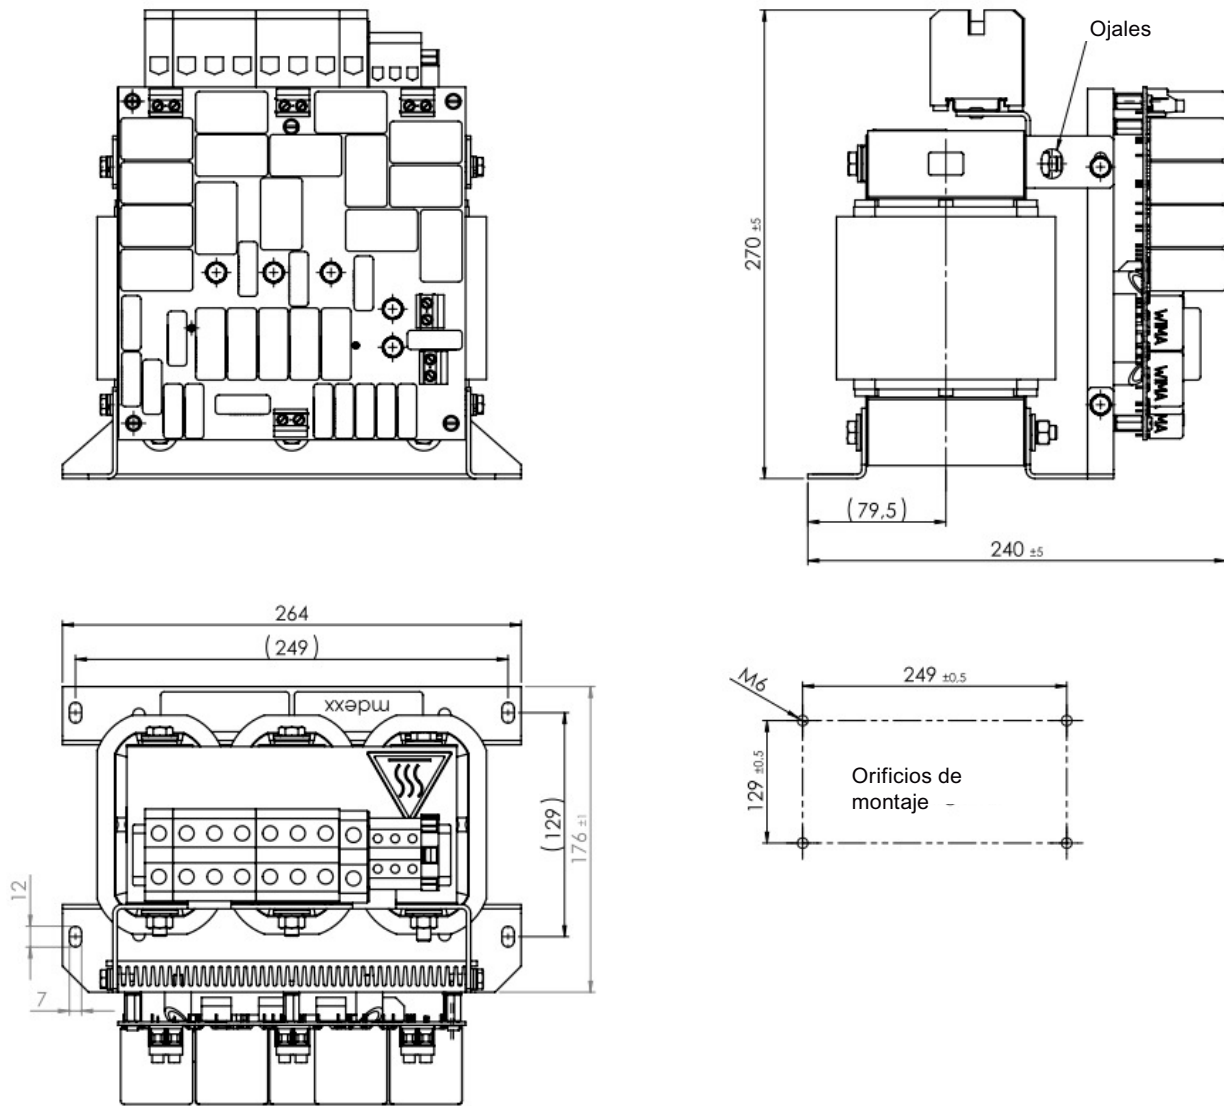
Dimensiones de JTA:TEF1203-0HB
